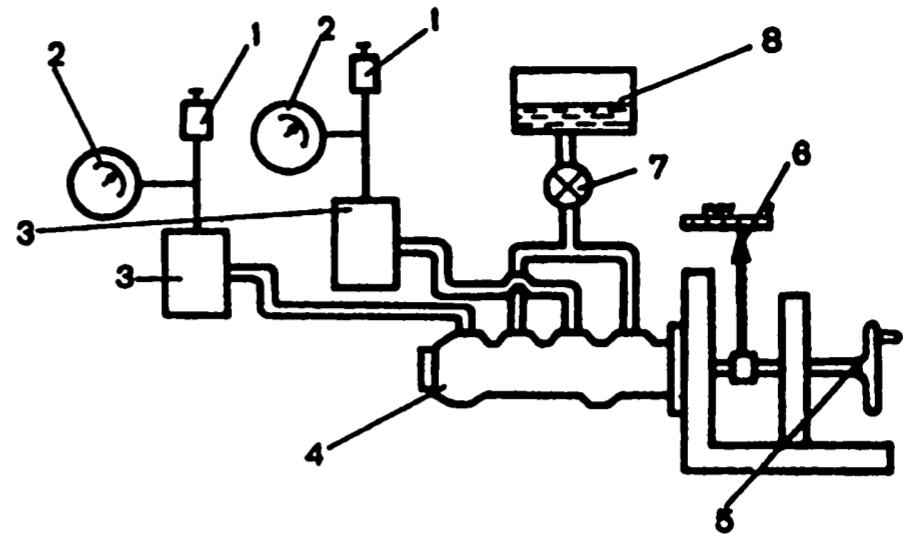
Схема проверки герметичности главного цилиндра: 1 - клапан для прокачки стенда; 2 - манометр; 3 - поглащающий цилиндр; 4 - главный цилиндр; 5 - маховик; 6 - указатель смещения толкателя; 7 - кран; 8 - сосуд
